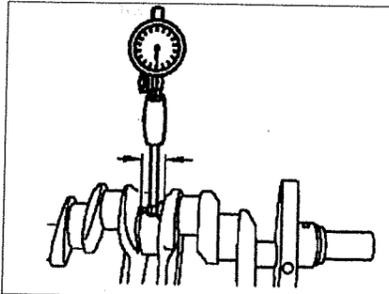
Измерение ширины шейки коренного подшипника.
